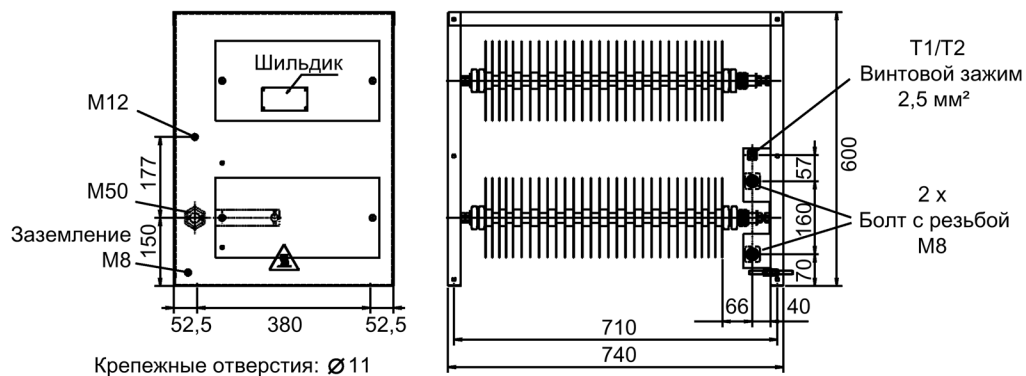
Габаритный чертеж тормозного резистора 25 кВт, 125 кВт (опция L61 / L64)
